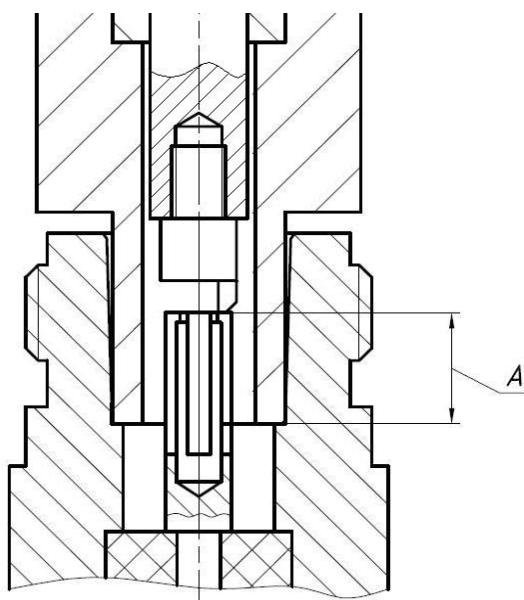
Проверка размера «A» соединителя «розетка»
